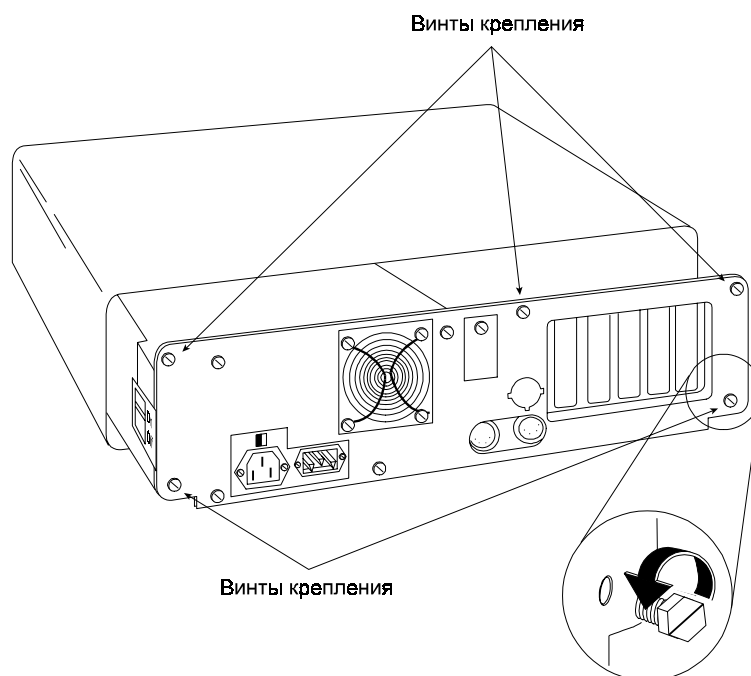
Расположение винтов крепления крышки корпуса AT
